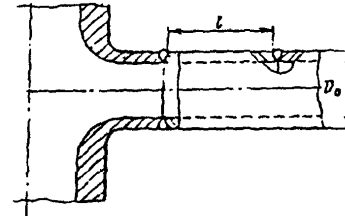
Расположение сварных швов при приварке трубопровода к патрубку
